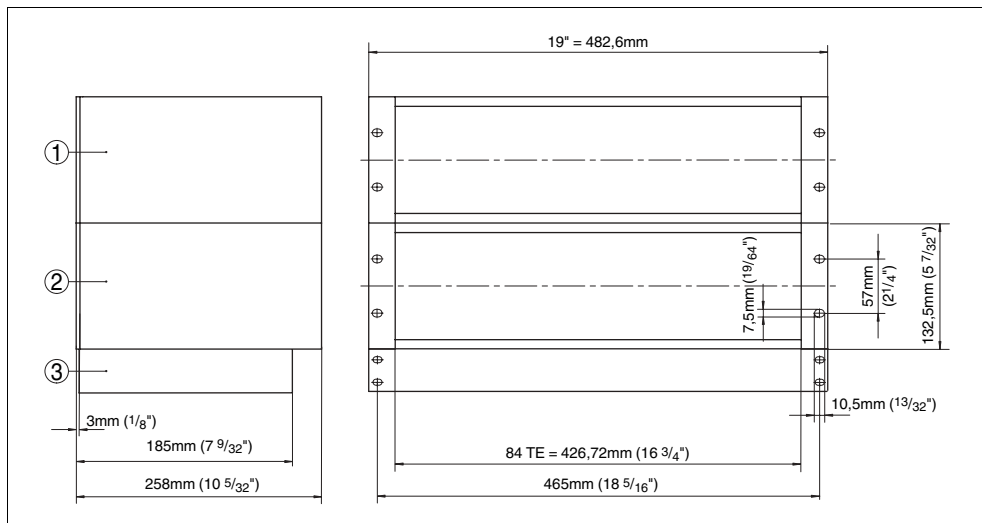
Размеры монтажного корпуса BGT LOG 571
